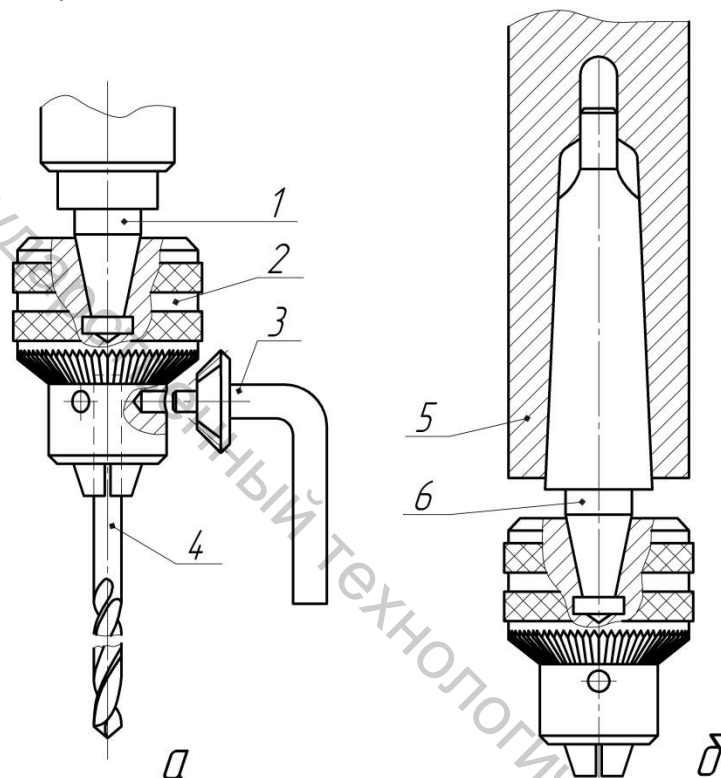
Схема установки стандартного сверлильного патрона на шпинделе настольно-сверлильного (а) и в шпинделе вертикально-сверлильного (б) станков: 1, 5 – шпиндели; 2 – патрон; 3 – ключ привода зажима; 4 – сверло; 6 – переходный хвостовик
